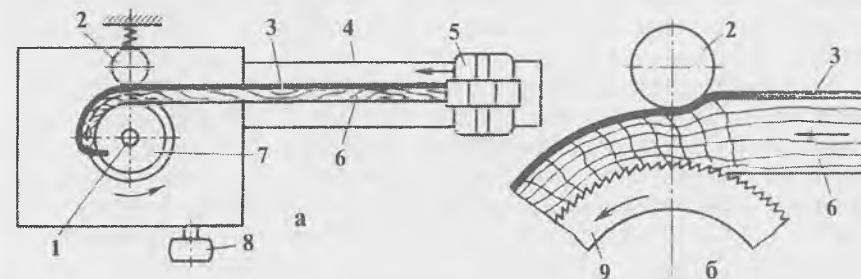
Схема гнутья заготовок в гнутарных станках на замкнутый контур:
